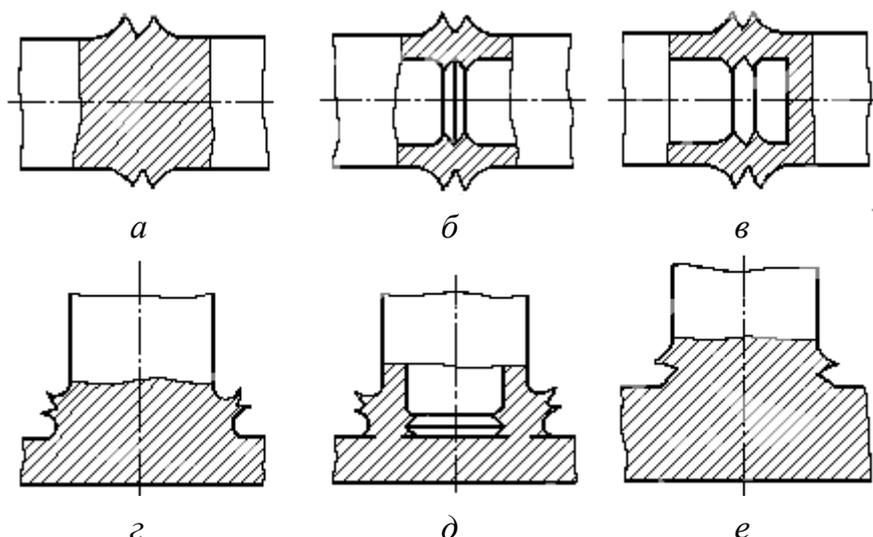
Типы сварных соединений, выполняемых сваркой трением
